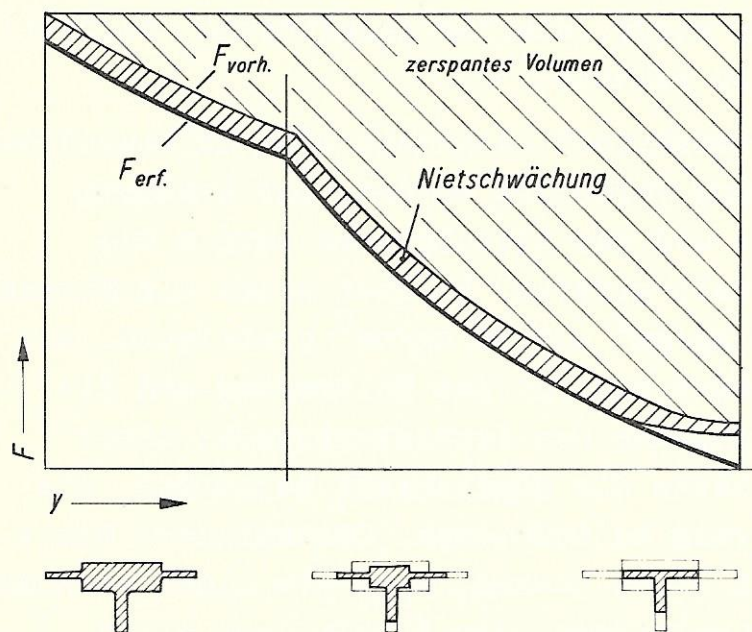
T-Gurt gefräst, Anpassung der Querschnitte
